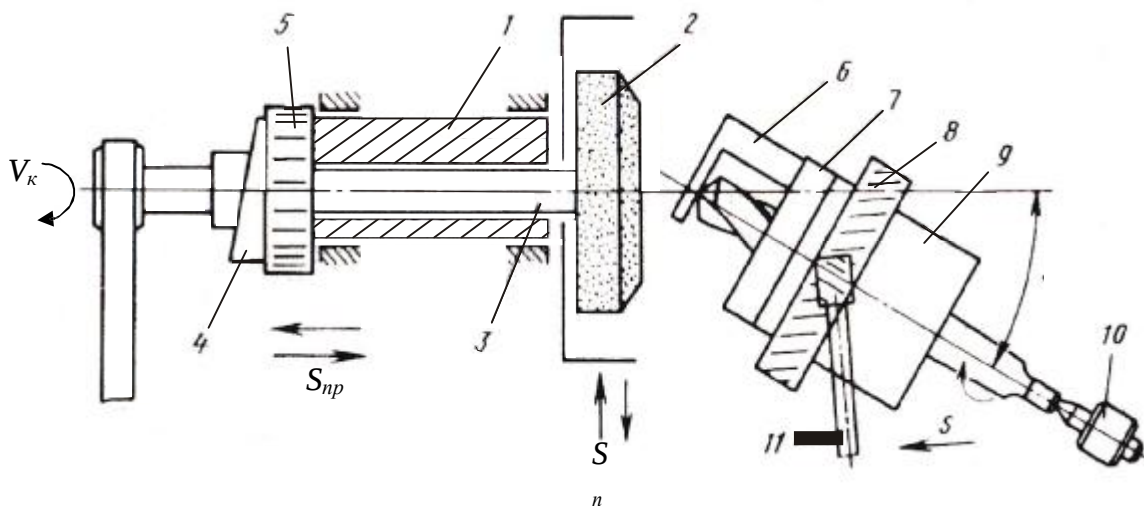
Схема заточування свердла по гвинтовій поверхні
